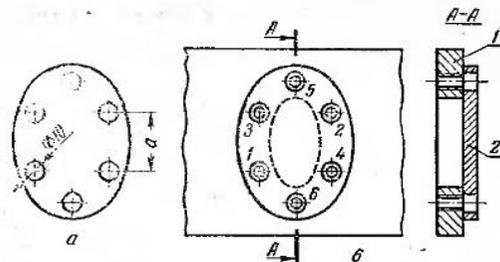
Заделка пробойны с наложением металлической заплаты:
